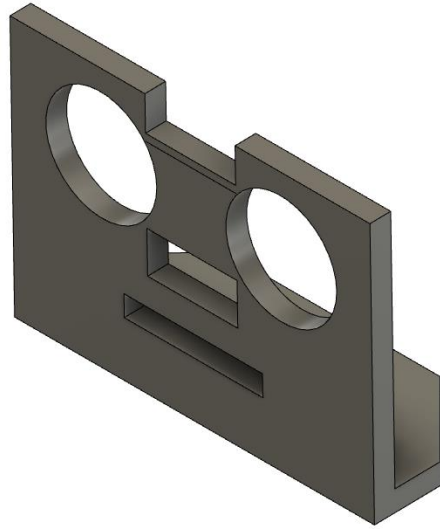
Diseño de los soportes de motor en el CAD Fusión 360 en vista isométrica
